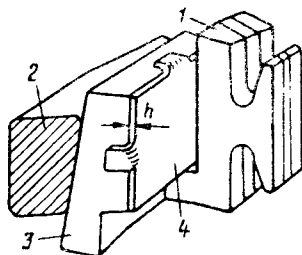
Сборка коллектора с пластмассовым корпусом;
